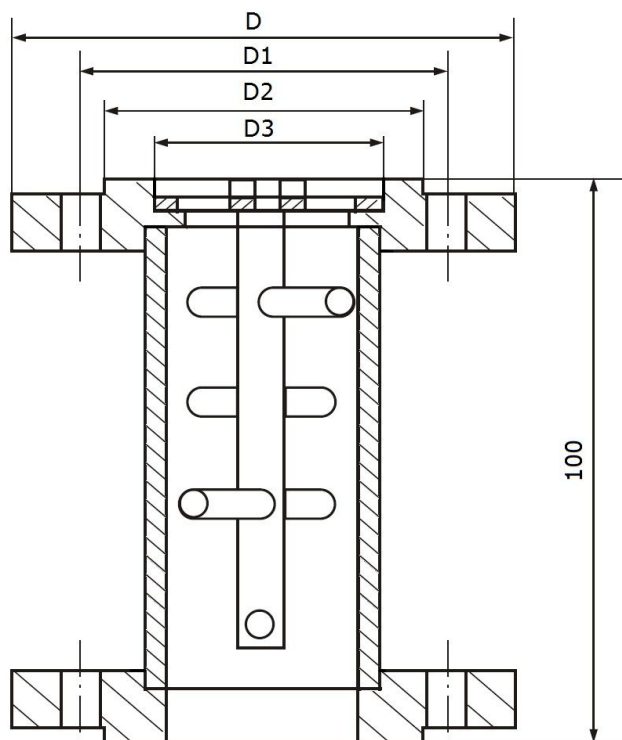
Габаритные и присоединительные размеры магнитных фильтров
